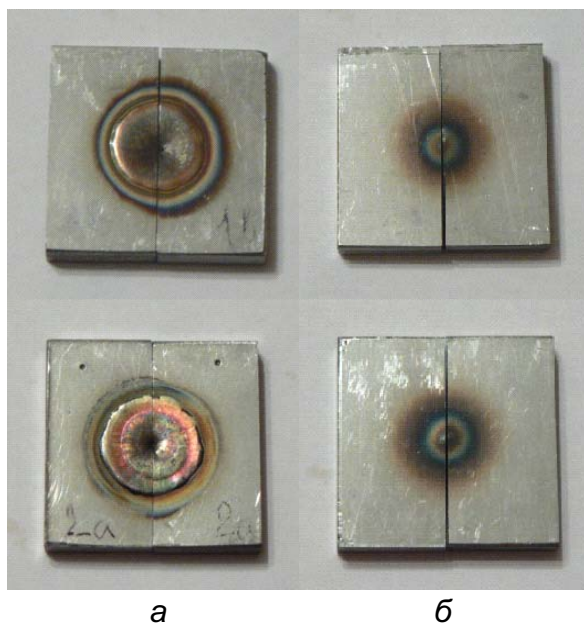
Образцы сварных соединений нержавеющей стали 12X18H10T. а – вид со стороны проплава, б – вид с лицевой стороны.
